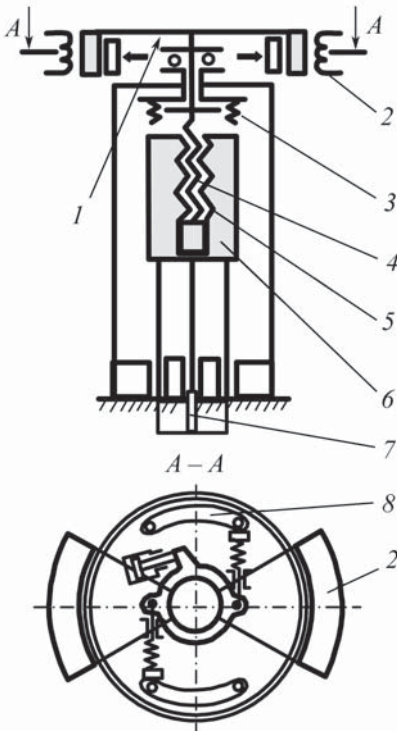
Схема винтового пресса с дугостаторным приводом:
